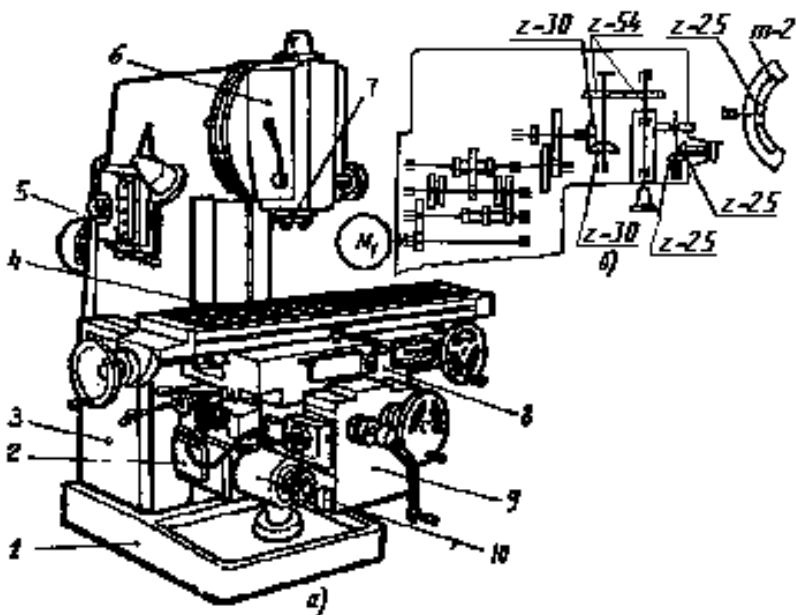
Вертикально-фрезерный станок мод. 6Л12П:
